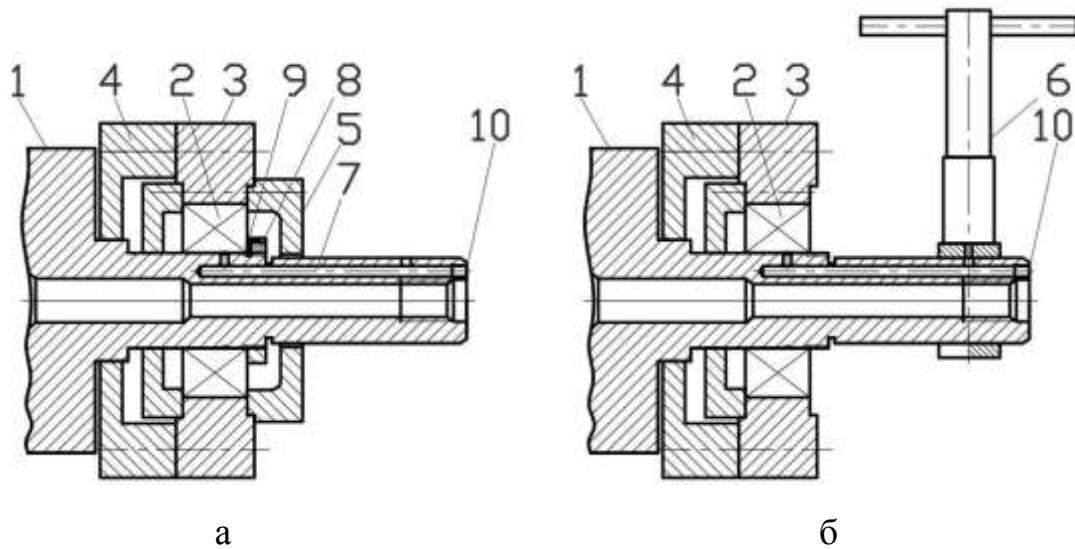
Зняття підшипника з робочого вальця.
